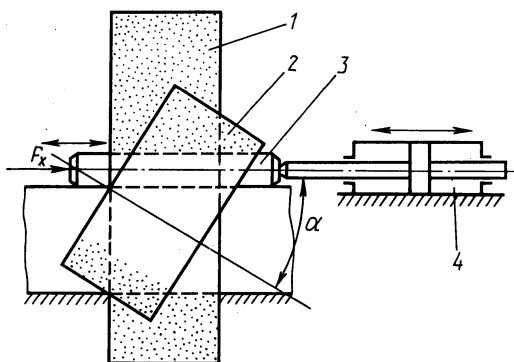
Схема бесцентрового врезного шлифования с осциллирующим перемещением изделия: 1 — шлифовальный круг; 2 — ведущий круг; 3 — обрабатываемая деталь; 4 — гидроцилиндр выталкивателя
